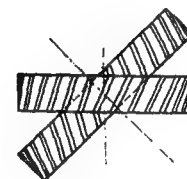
Juego de engranajes helicoidales para transmisión entre ejes que se cruzan
